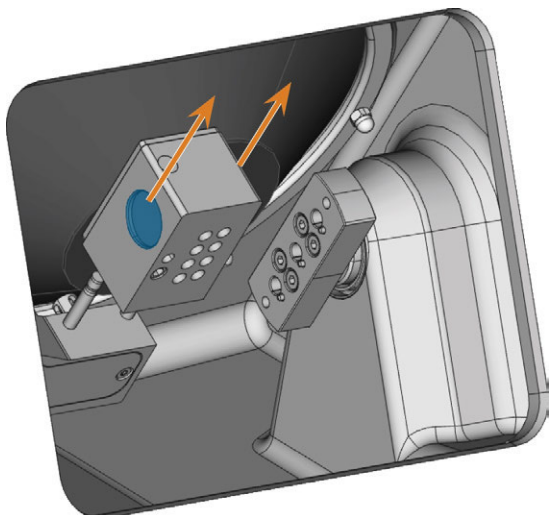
Das Werkzeugmagazin herausziehen (linke Griffmulde blau eingefärbt)
